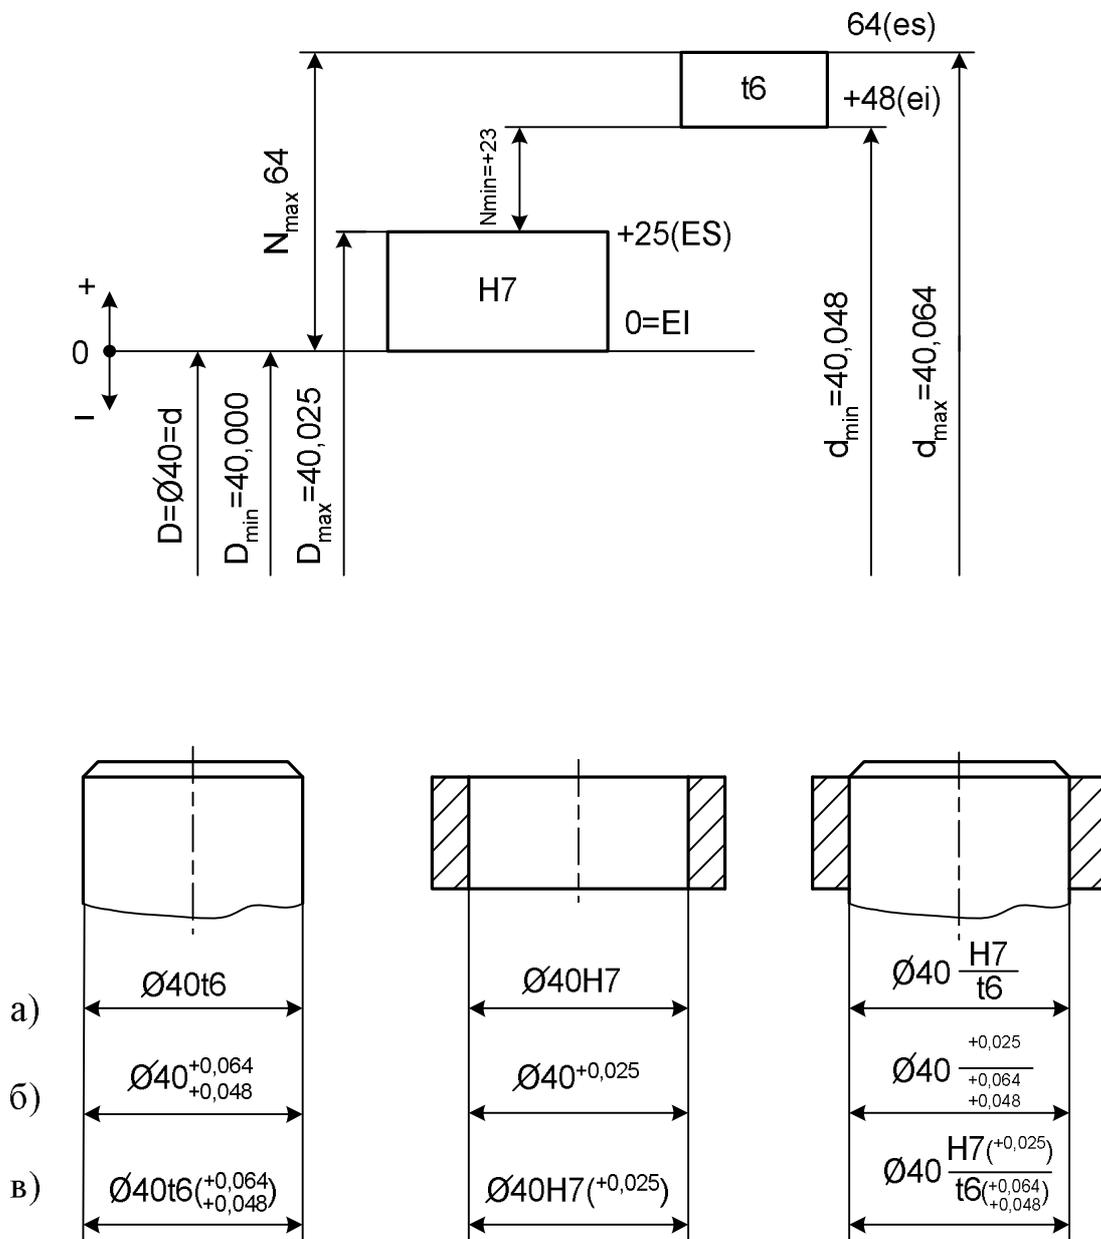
Схема полей допусков и эскизы деталей соединения  $\varnothing 40$  H7/t6.
